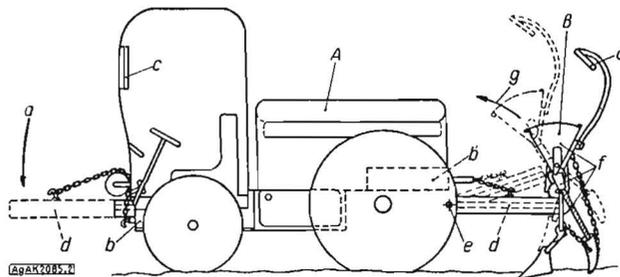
Seitenansicht der neuen Kombination Schlepper-Anbaudrillmaschine. A Schlepper mit Fahrersitz vorn, B Mechanisierte Drillmaschine, a Drillmaschine kann auch vor dem Schlepper angebracht werden, b Hydraulik, c Rückspiegel, d Zapfwelle, e Drehpunkt und Ausklinkung der Zapfwelle beim Heben, f Saatkasten, Sägehäuse und Saatlleitung aus durchsichtigem Kunststoff, g Heben und Senken
